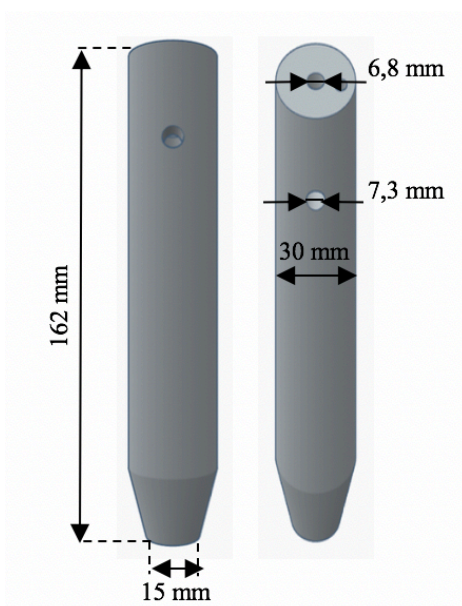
Esquema e dimensões do revestimento dimensionado para o dispositivo.
